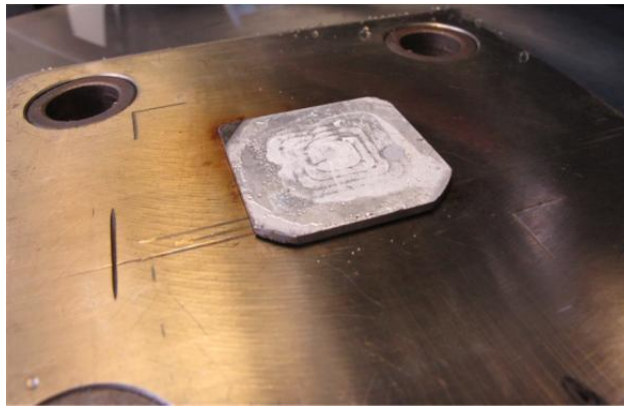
Exemple de résultat après le premier assemblage. La plaquette de matériau TE (milieu sur la photo) est soudée aux plaques céramiques (non visibles ici car en dessous de la plaquette TE) qui sont collées à la plaque en inox du système d'assemblage (visible en dessous de la plaquette de matériau TE).
